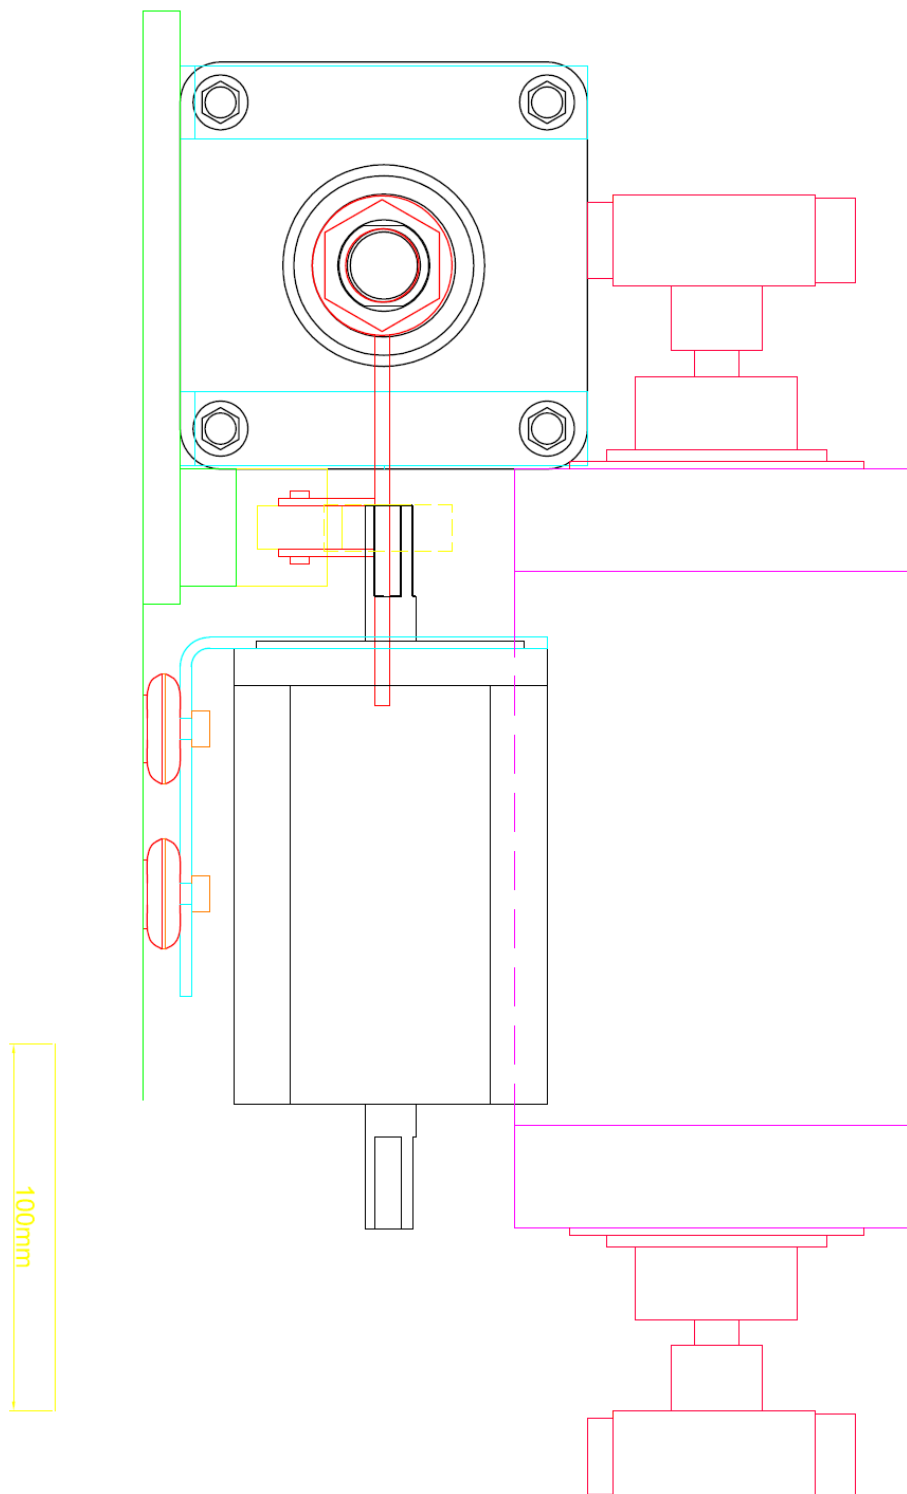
SIMVENT, parte mecánica vista frontal - fuente SIMVENT
